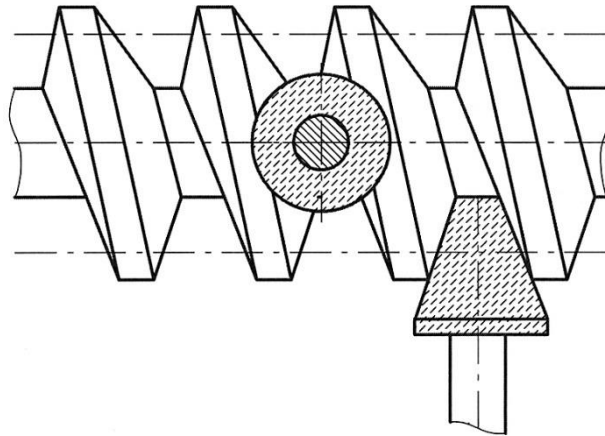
Схема шліфування евольвентного черв'яка чашечним кругом
